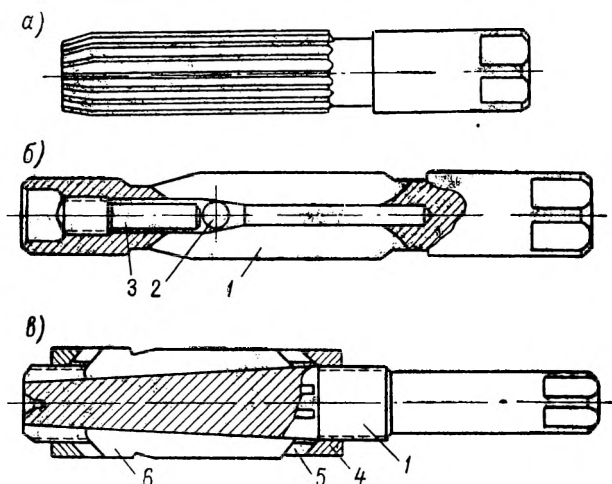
Типы ручных разверток: а — жесткая; б — раздвижная; в — регулируемая.
